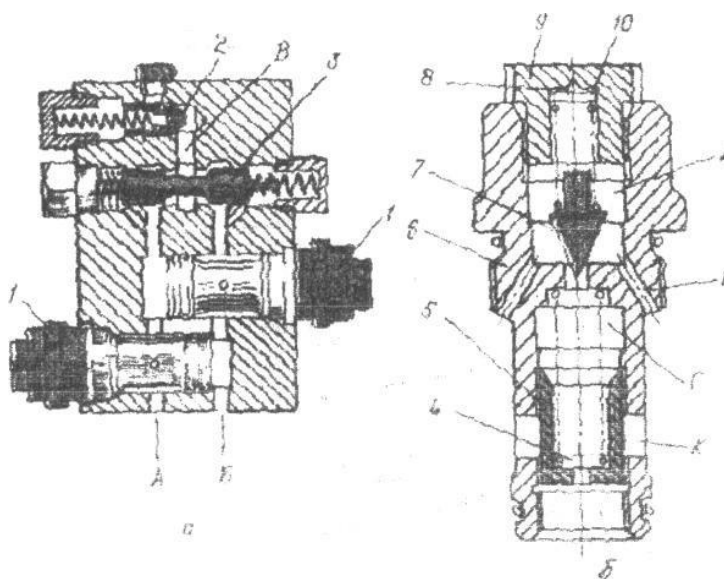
Клапанная коробка: а) блок клапанов; б) клапан высокого давления; А, Б, В, И, К, - каналы; Г, Д, - полости; - клапан высокого давления; 2 - переливной клапан; 3 - золотник; 4,10 - пружины; 5 поршень; 6 - корпус; 7 - игла; 8 - регулировочные шайбы; 9 - пробка
